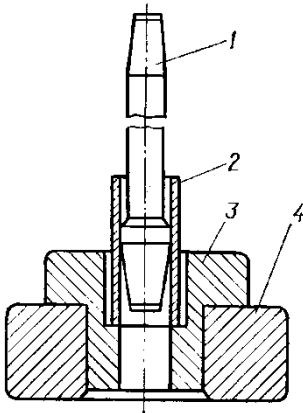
Пристрій для роздавання поршневих пальців: 1 – конусна оправка; 2 – поршневий палець; 3 – напрямна; 4 – підставка
